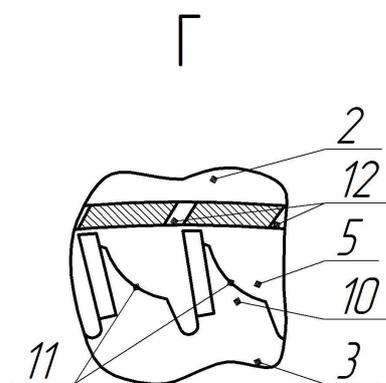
Схема зубчатого венца пилы с вогнутой тыльной частью зубьев: 2 – воздухоприемник; 3 – кольцевая пила; 5 – боковая направляющая пилы; 10 – зуб; 11 – тыльная часть зуба; 12 – сопло
